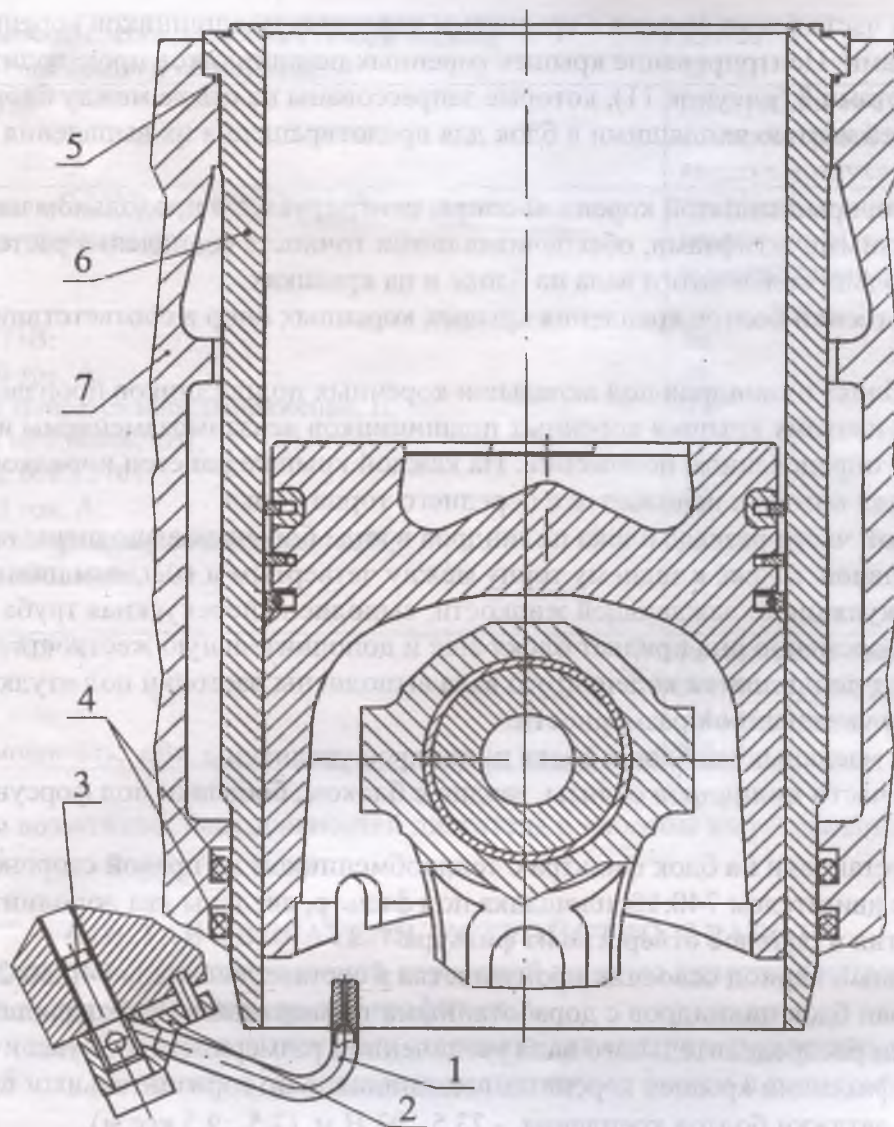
Установка гильзы цилиндра и уплотнительных колец:
